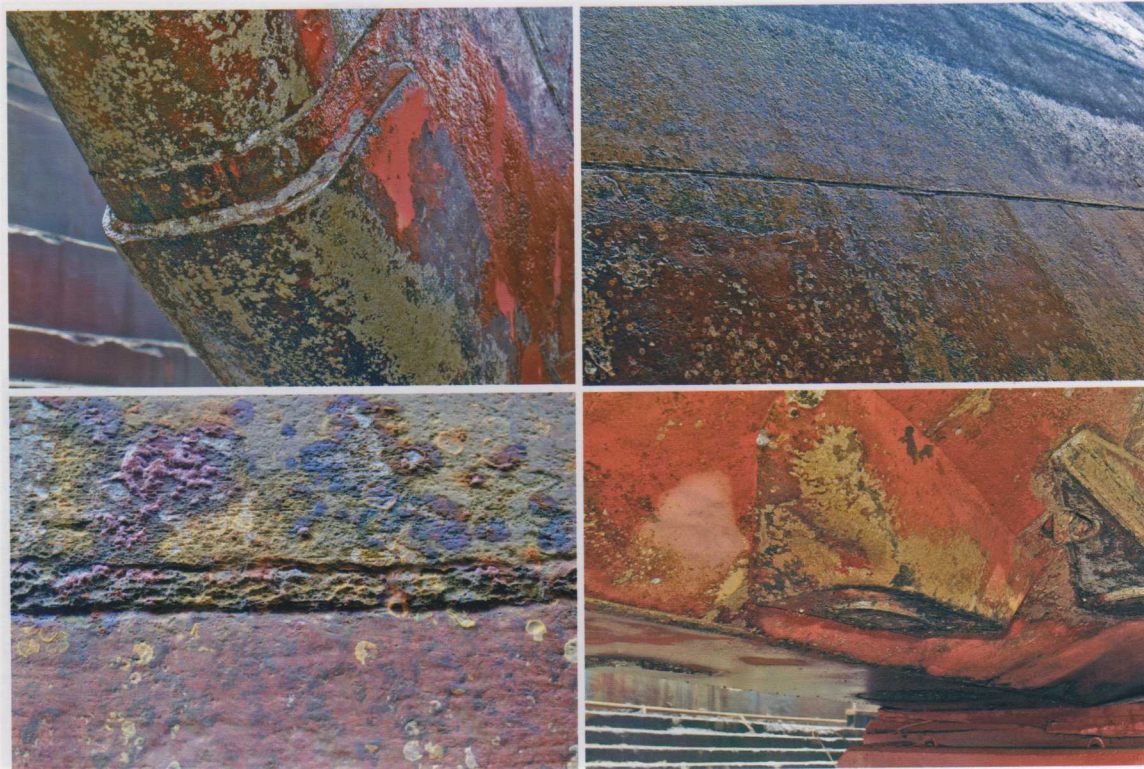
17. Состояние сварных швов наружной обшивки корпуса судна до ремонта.
